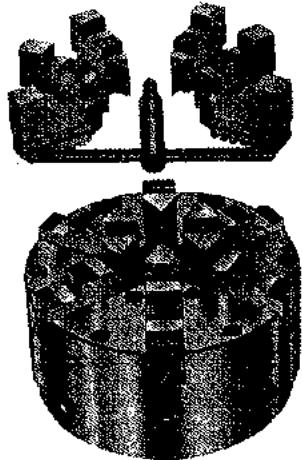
Plato combinado de seis mordazas (Buck Tool Co.).
